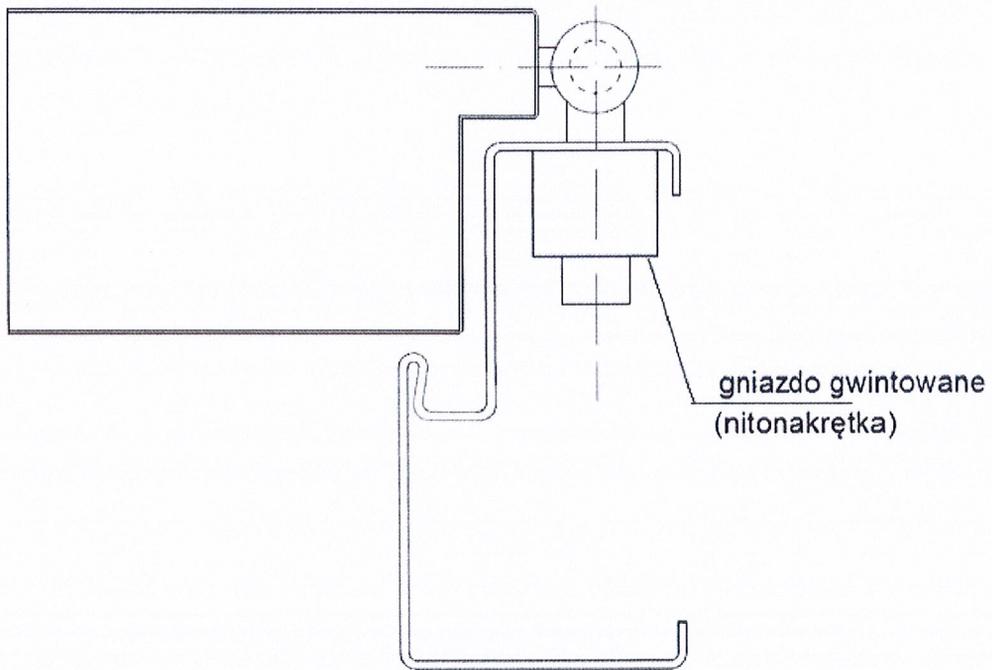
Befestigen der Scharniere im Türrahmenständer – Einschrauben der Scharniere in den Gewindesitz
